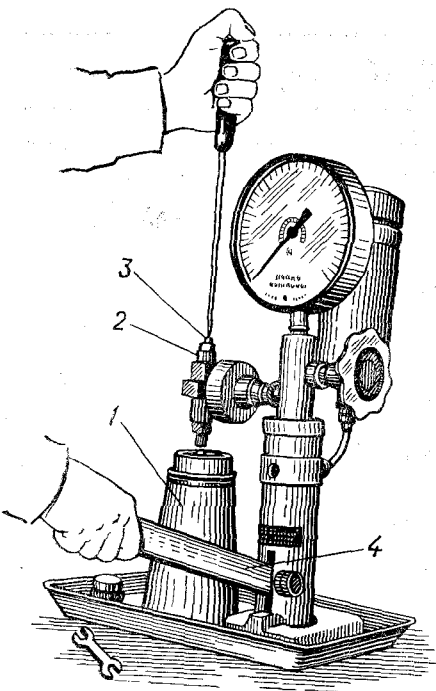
Регулювання форсунки на пристрої КИ-562:
